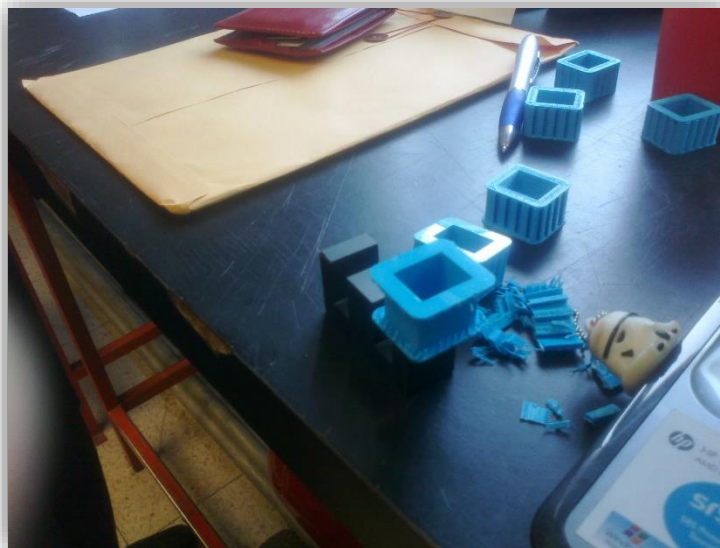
carretes de bobinas, hechos en impresora 3D.
